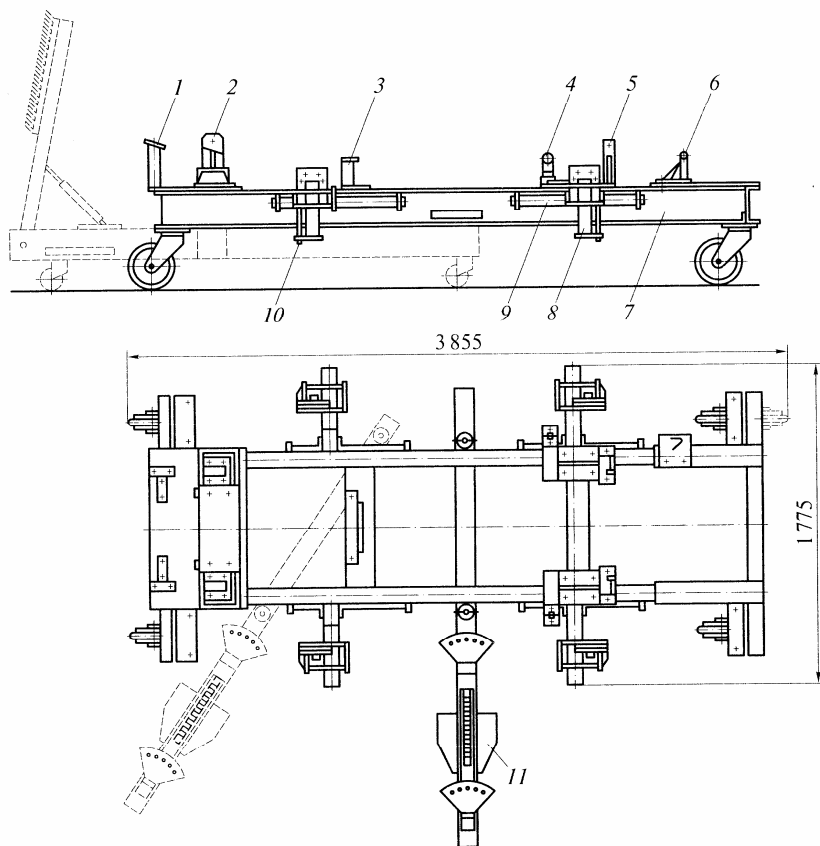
Передвижная установка БС-123.000 для правки и контроля кузовов легковых автомобилей: 1...6 – съемные опорные кронштейны; 7 – рама; 8 – стойки с зажимными приспособлениями; 9 – эксцентриковые валы; 10 – регулировочные винты; 11 – силовой элемент (устройство БС-124.000)
